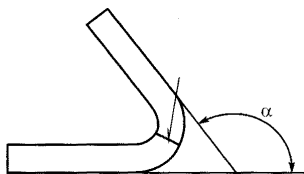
Сварное соединение. Образец для испытания на изгиб:
